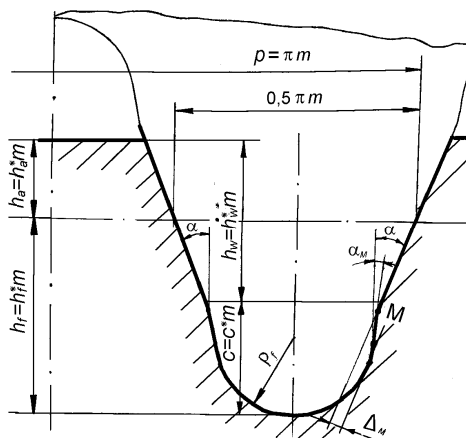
Специальный исходный контур зубчатого колеса с поднутрением ножки зуба и полнопрофильным закруглением впадины
